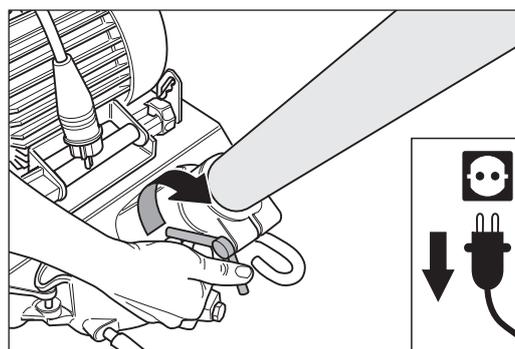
Nach dem Einbau des Führungsrohrs die Flügelmutter am Maschinengehäuse sorgfältig festziehen.
